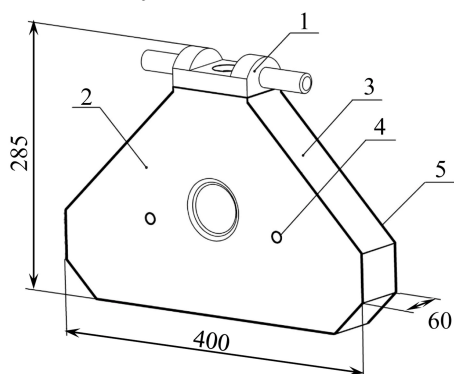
Схема корпуса: 1 – основание; 2 – пластина; 3 – бортик; 4 – втулка; 5 – сварные швы
